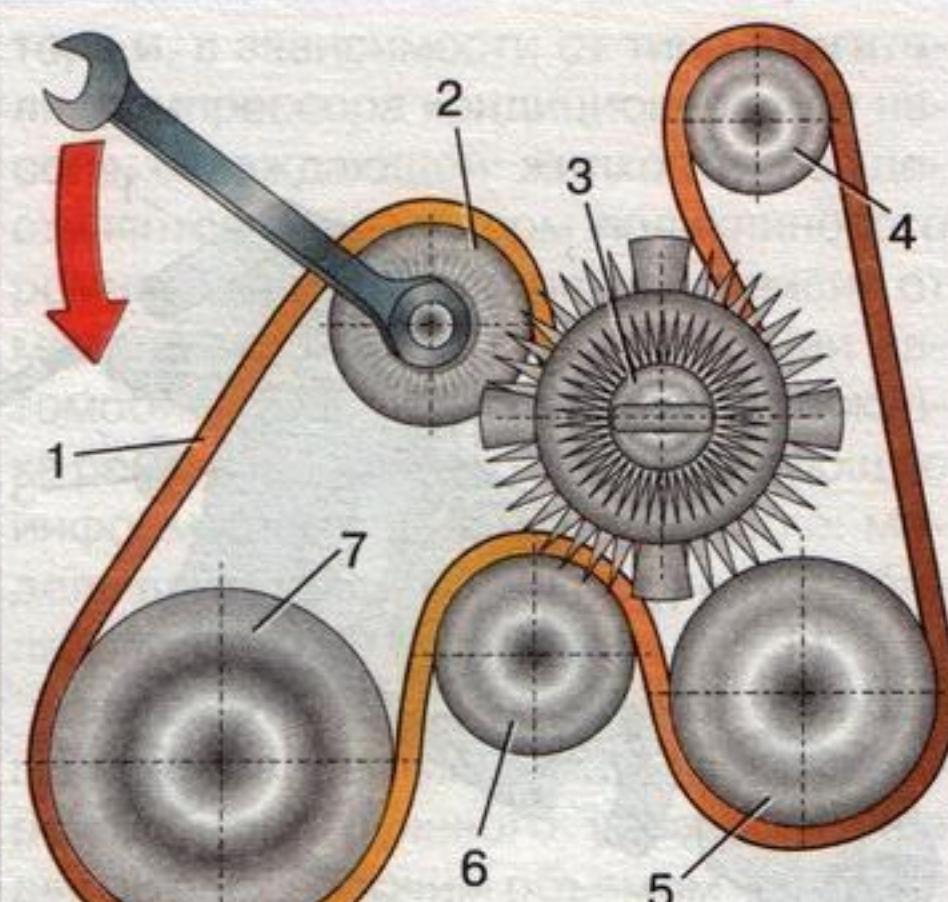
Схема установки ремня привода агрегатов дизельного двигателя рабочим объемом 1,9 л: 1 – ремень привода агрегатов; 2 – натяжной ролик; 3 – шкив вентилятора охлаждения двигателя; 4 – шкив генератора; 5 – шкив насоса гидроусилителя рулевого управления; 6 – шкив коленчатого вала
